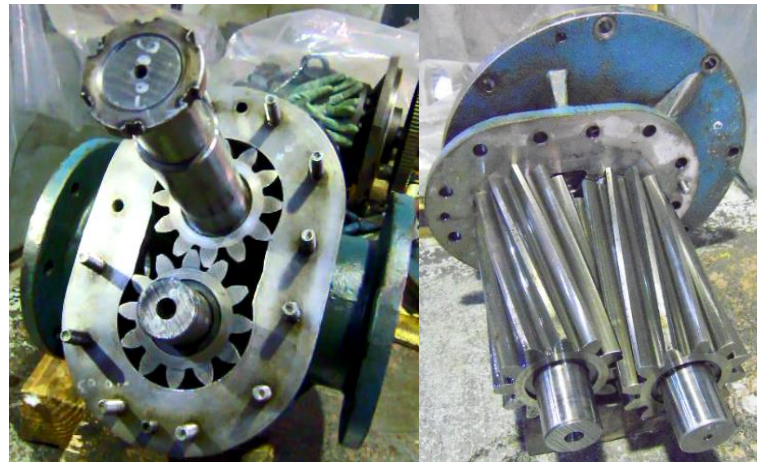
Pompe à huile à engrenage (Moteur CMI).
